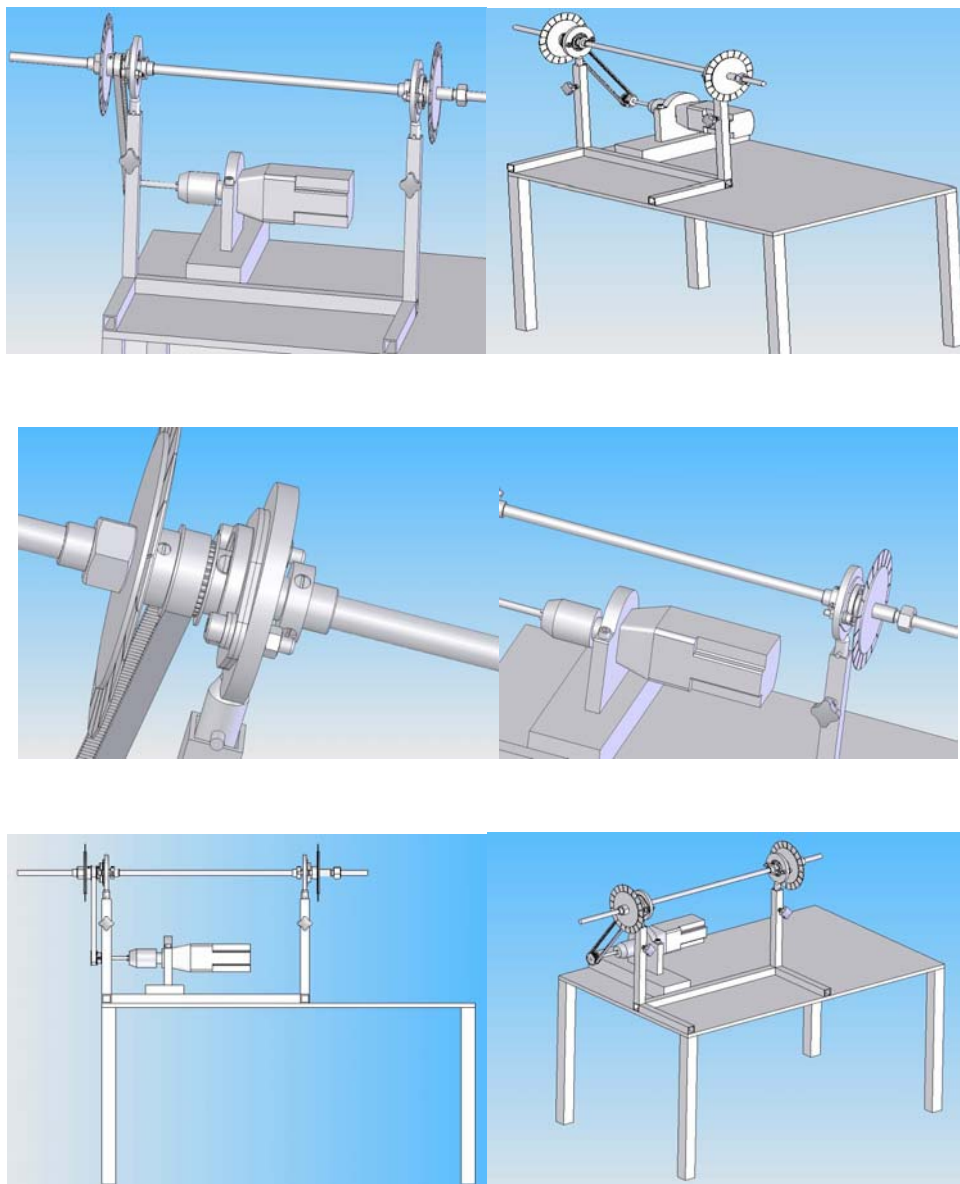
Technický výkres bal. kyv.v rovnovážné poloze
